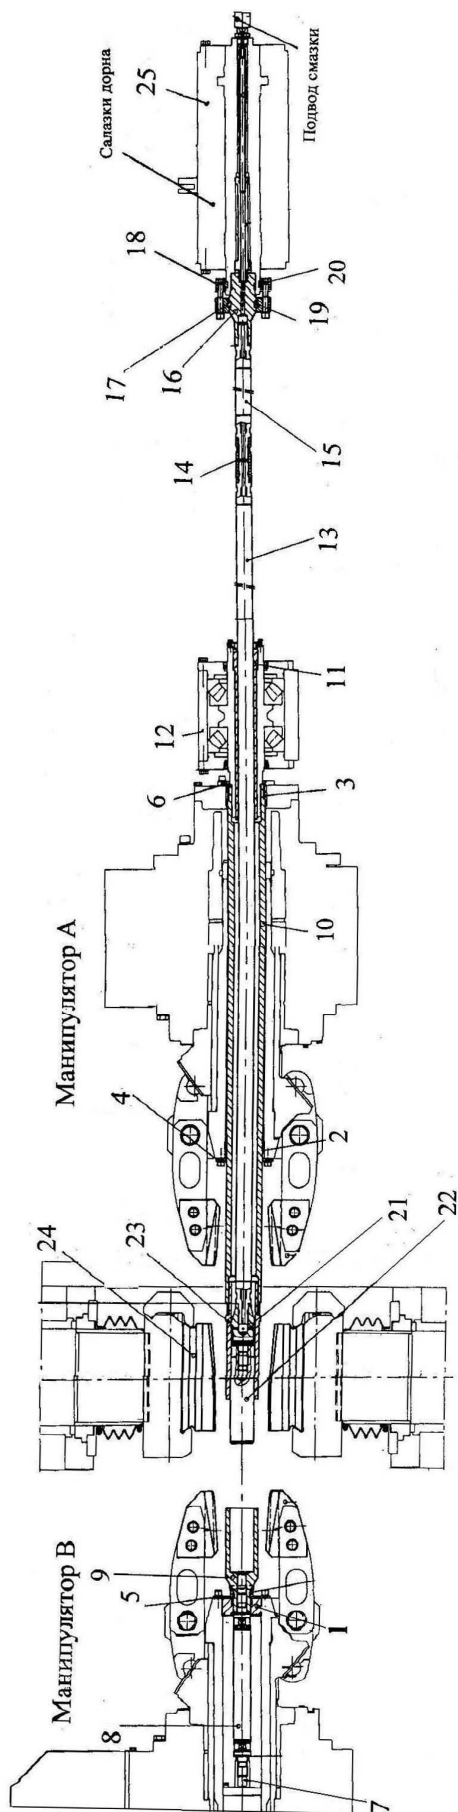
Схема установки инструмента и приспособлений для холоднойковки труб
